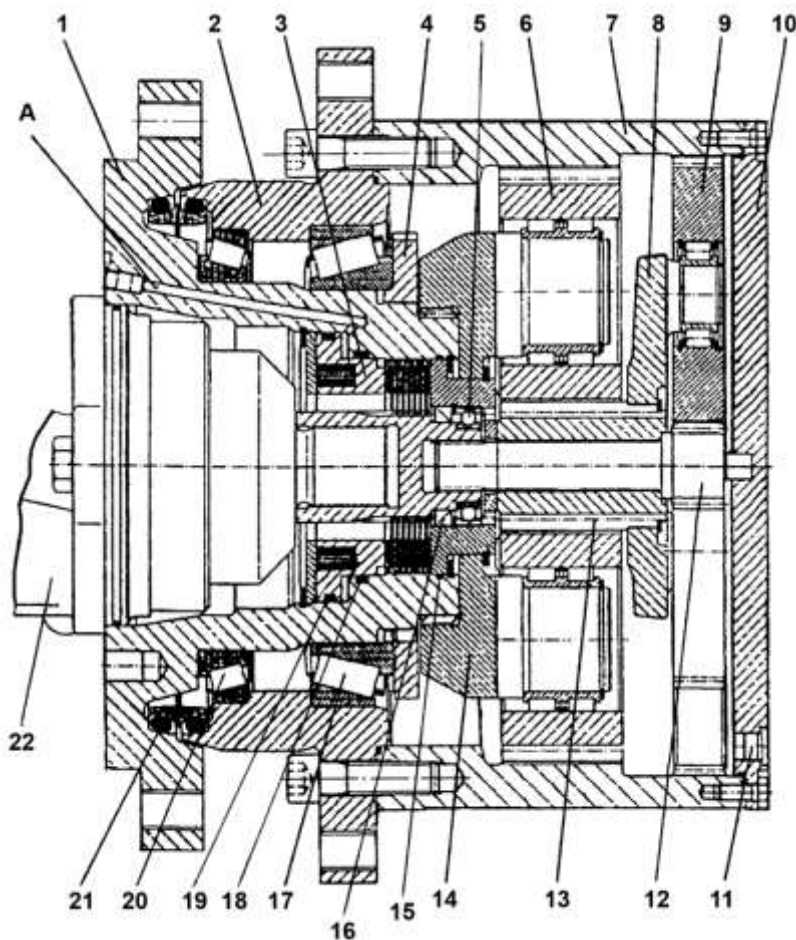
Планетарний редуктор ведучої зірочки бортової трансмісії
